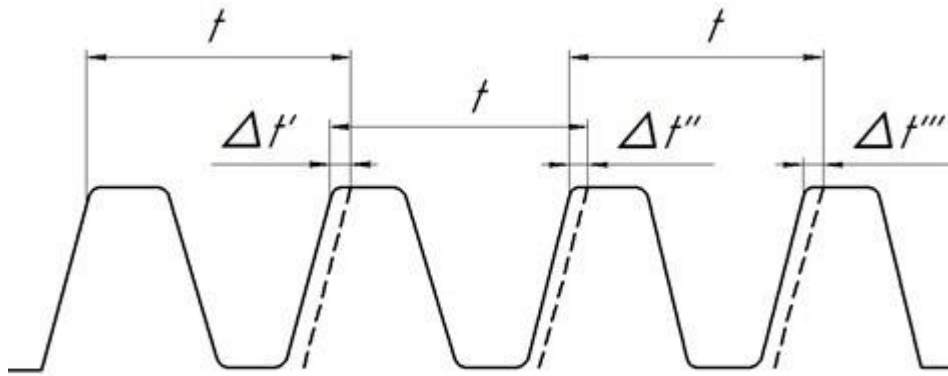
Схема контролю похибки осьового кроку черв'ячної зуборізної фрези
